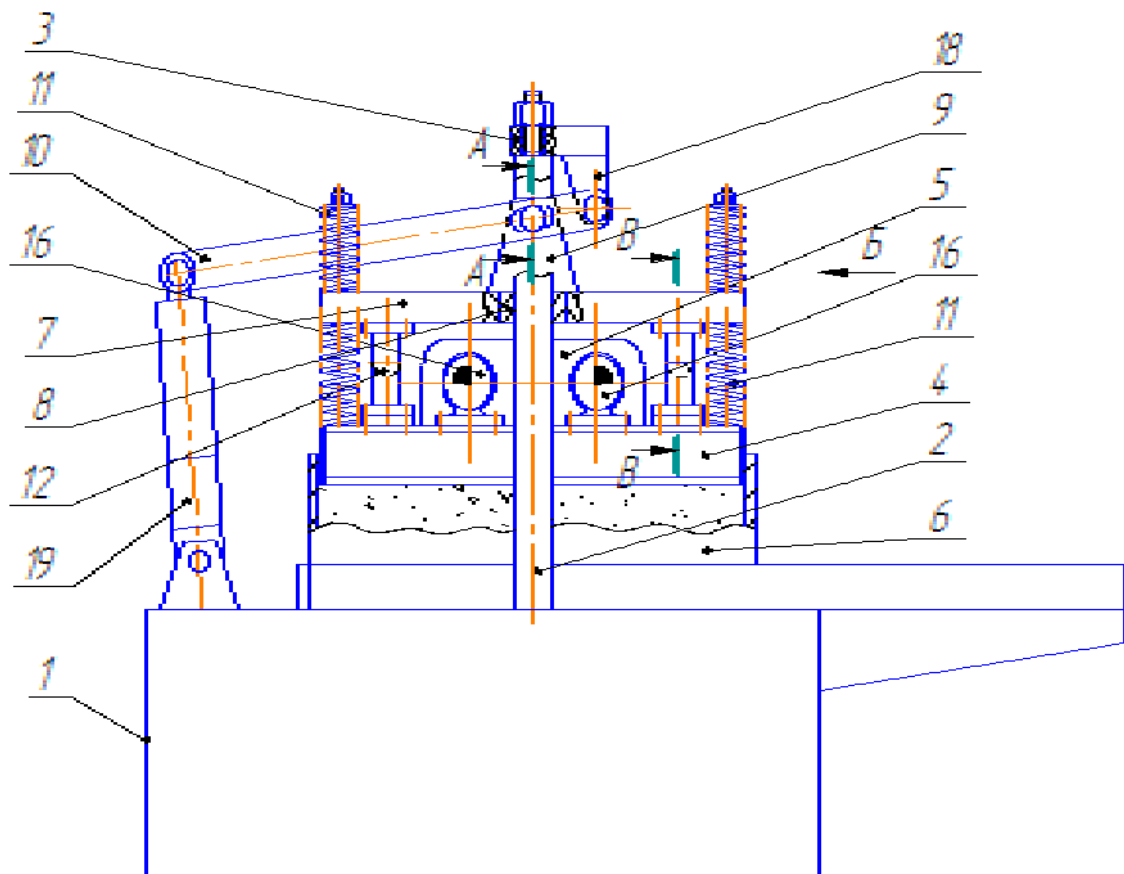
Общий вид вибропресса для формования изделий из конструкционных порошковых материалов с жестко-упругими ограничителями
